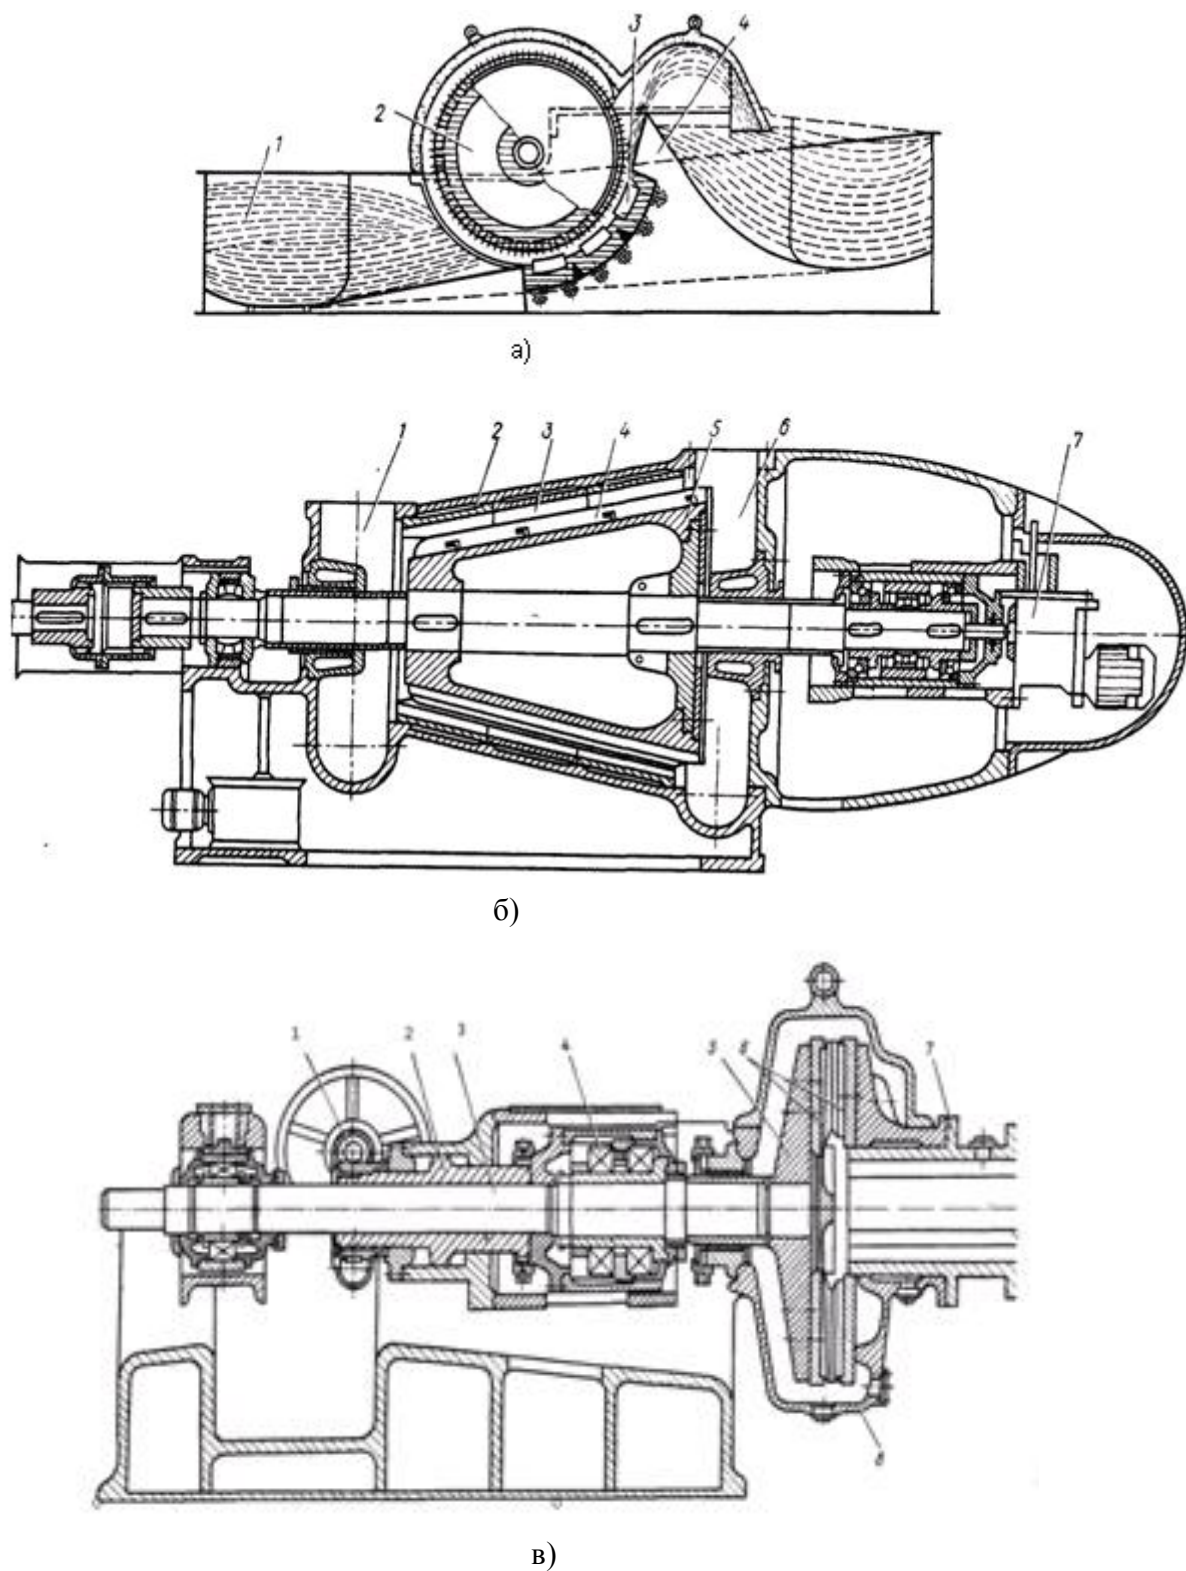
Основные типы ножевых размалывающих машин: а — ролл: 1 — ванна; 2 — ножевой барабан; 3 — планка с ножами; 4 — горка; б — коническая мельница: 1 — входная полость; 2 — корпус статора; 3, 4 — ножи статора и ротора; 5 — кольцевая стяжка для крепления ножей ротора; 6 — выходная полость; 7 — механизм присадки; в — дисковая мельница: 1 — механизм присадки; 2 — гидроцилиндр механизма присадки; 3 — вал; 4 — подшипники; 5 — диск; 6 — ножевая гарнитура ротора и статора; 7 — входной патрубок; 8 — размольная камера
